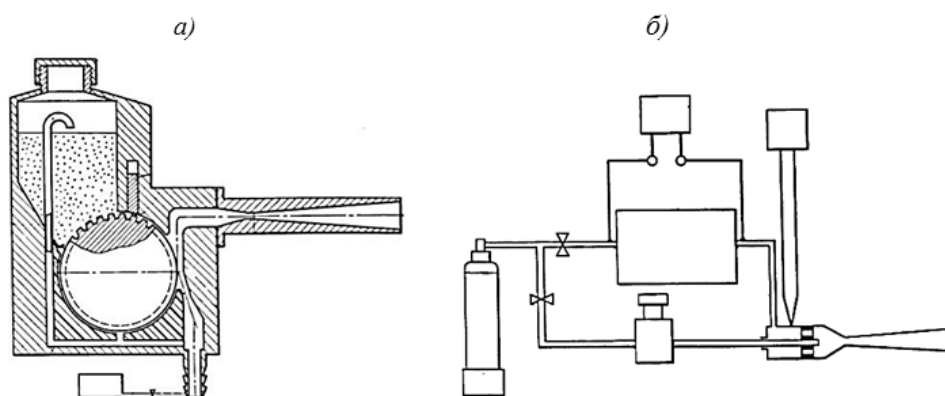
Устройство для нанесения покрытия на поверхность изделия:
